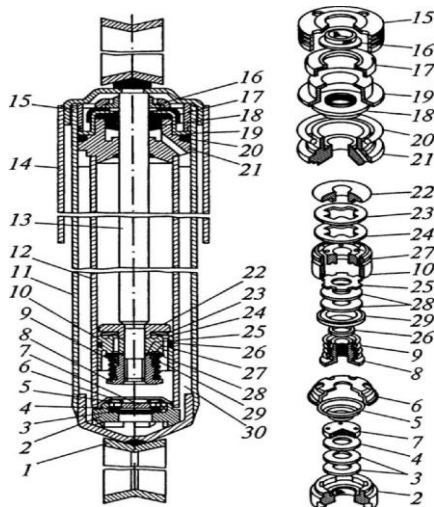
Телескопічний гідравлічний амортизатор: 1 - вушко; 2 - днище; 3,4,25,28 - диски; 5,9,23 - пружини; 6,19 - обойми; 7,22 - тарілки; 8,15 - гайки; 10 - поршень; 11 - резервуар; 12 - циліндр; 13 - шток; 14 - кожух; 16,27 - кільця; 17,18,20 - ущільнювач; 21 - втулка; 24,29 - клапани; 26 - шайба; 30 – камера.
